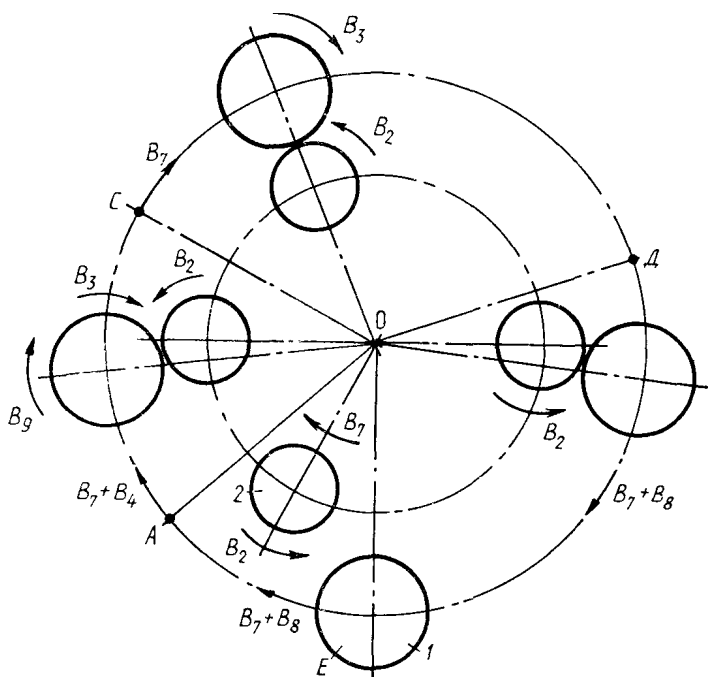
Способ зубодолбления при непрерывном транспортировании пары долбяк – заготовка
